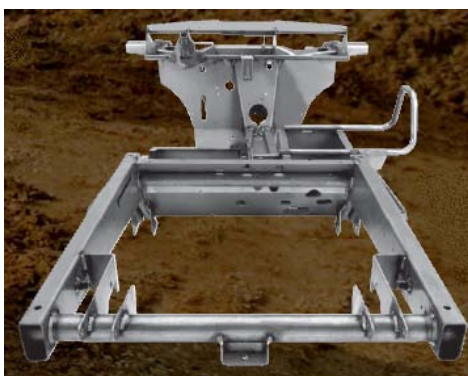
New Holland Rustler 125 s pevnou zadní nápravou [26]
